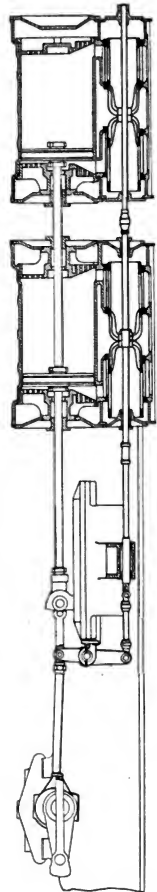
Ladepumpen - Steuerung der Siegener Maschinenbau - Aktiengesellschaft in Siegen.
